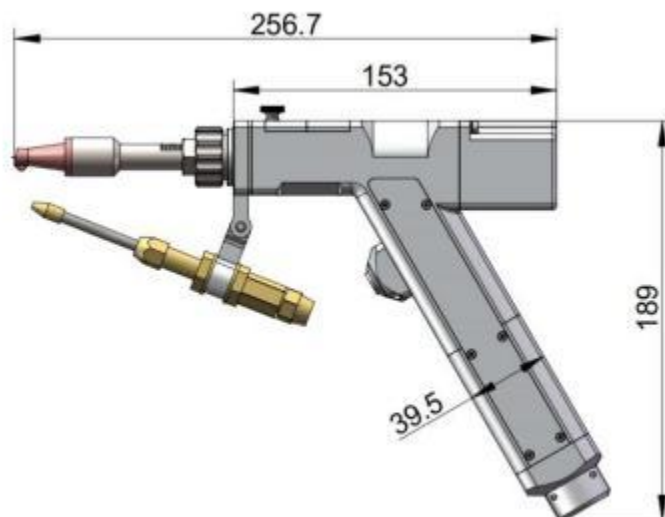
A120/A150 чертеж сварочного аппарата
